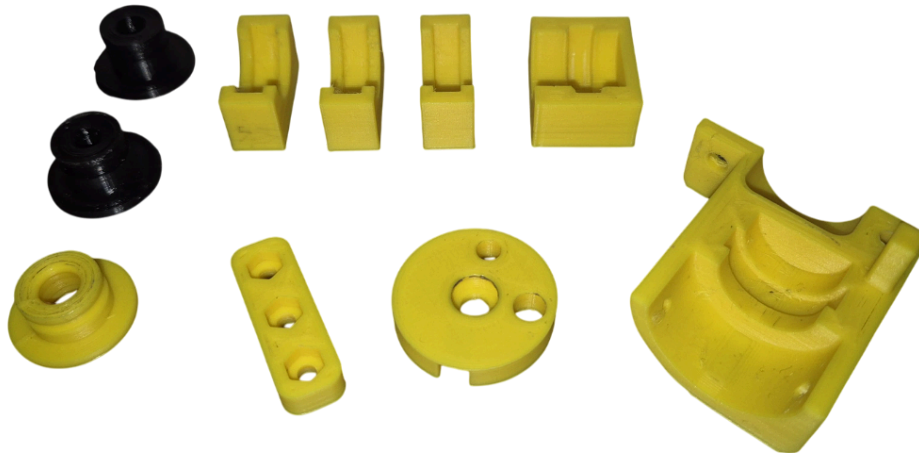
Photo de divers prototypes imprimés en 3D FDM
